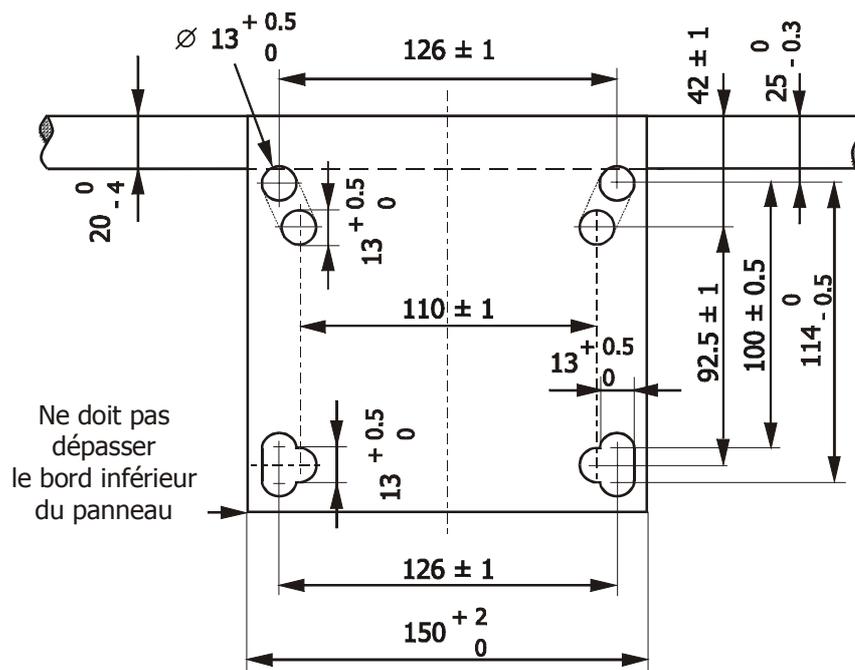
Plaque de montage de l'anneau pour des paniers existants
